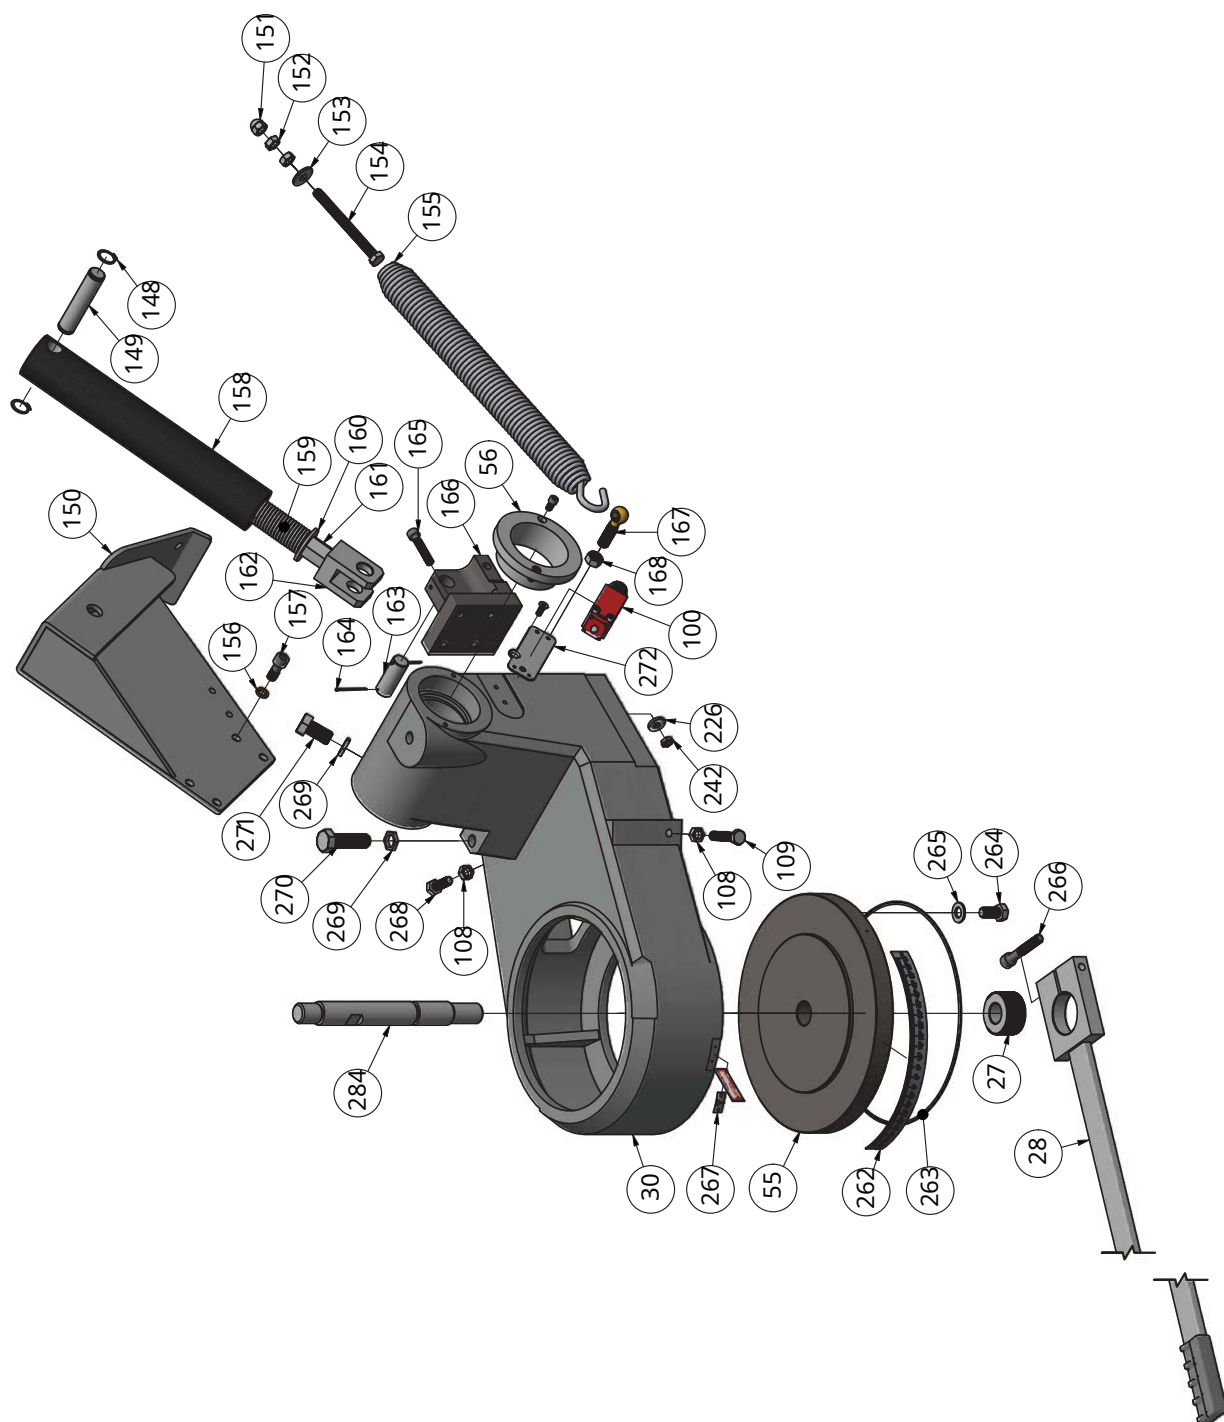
Explosionszeichnung - Dibujo de piezas de repuesto
